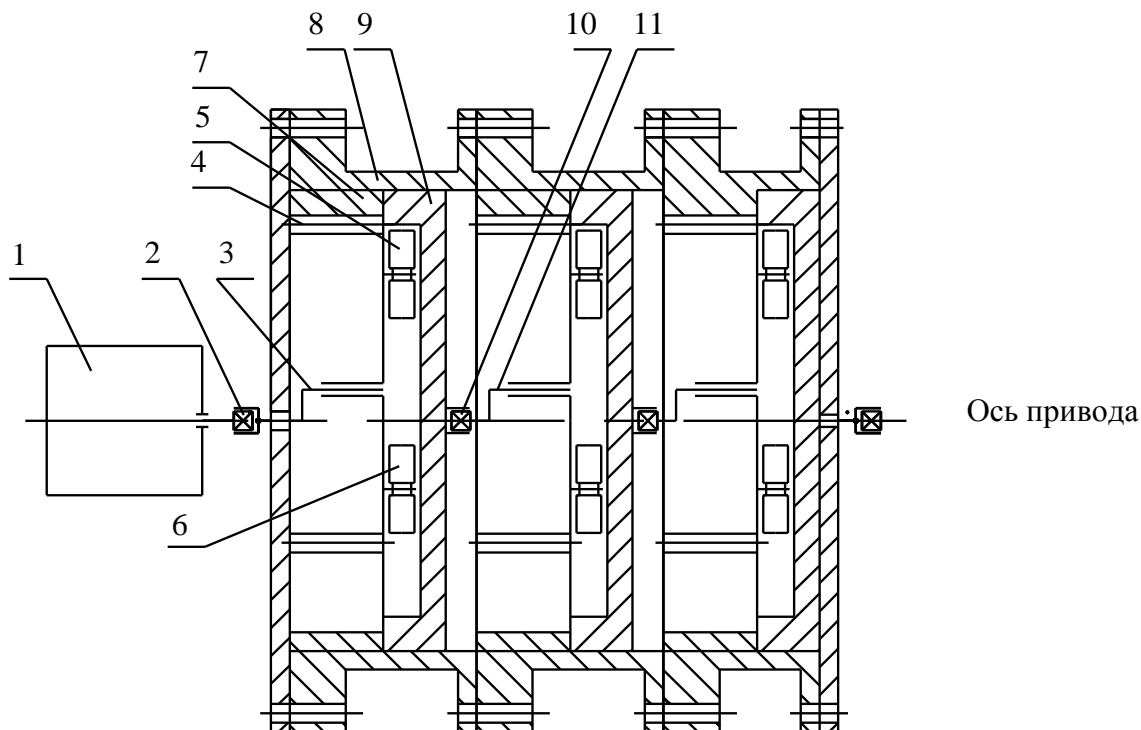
Схема планетарного привода вращательного движения вальцовочной машины
